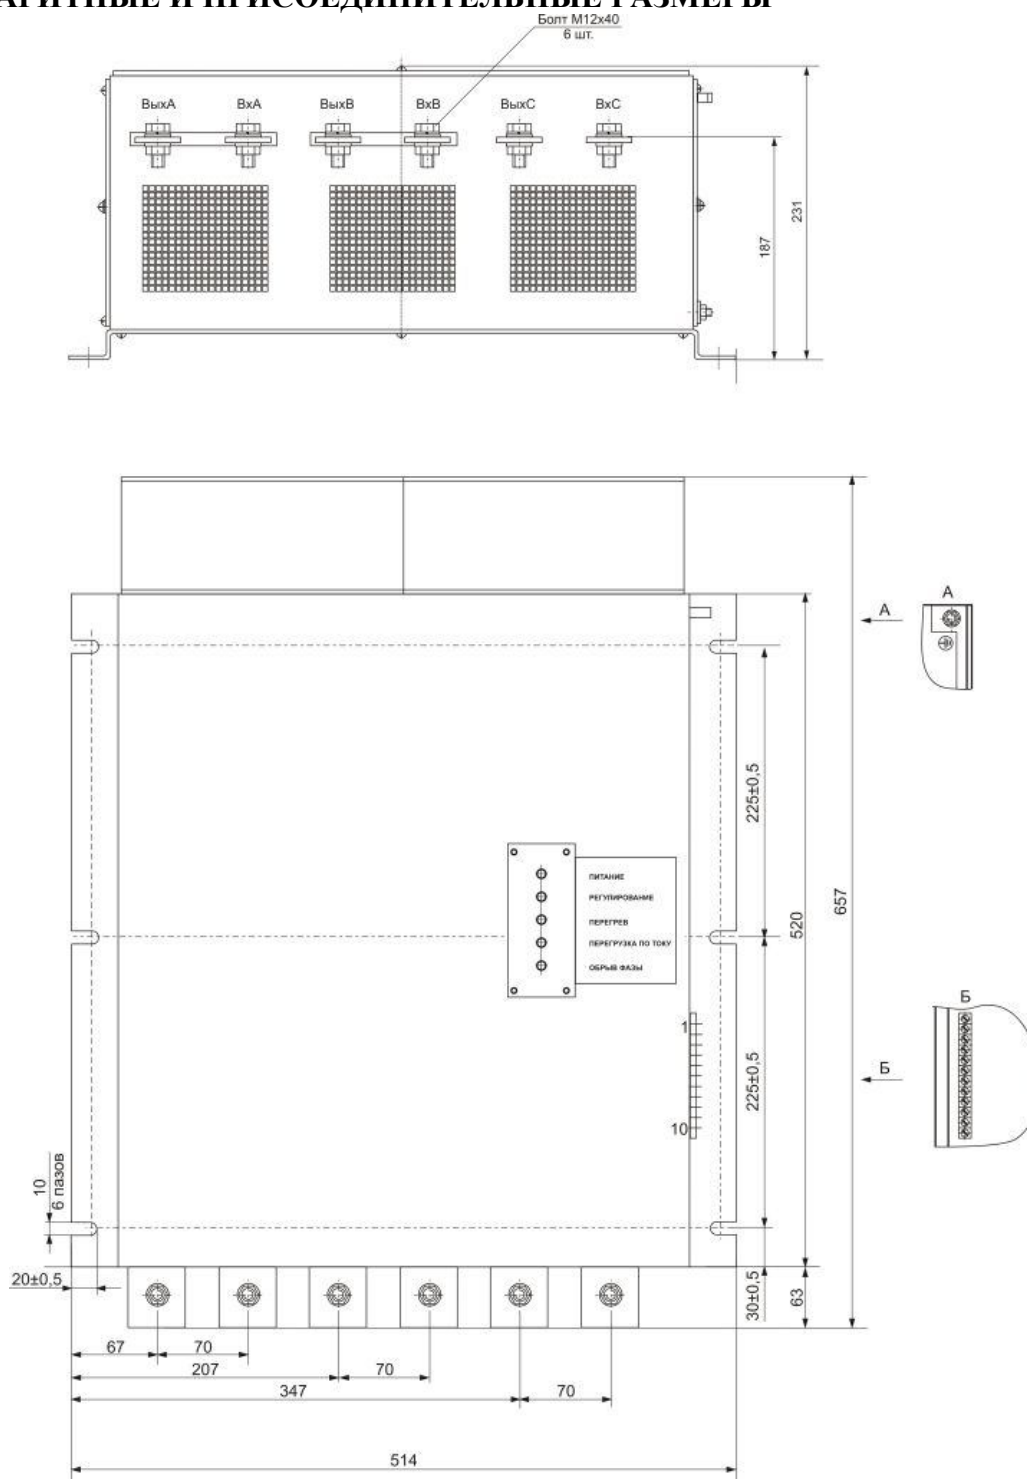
Габаритные и присоединительные размеры ТРМ
